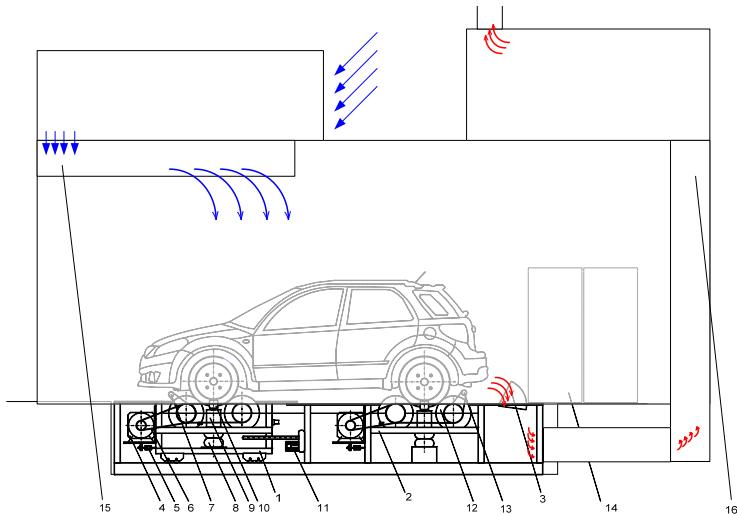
Универсальный финишный стенд для оценки качества сборки автомобилей
